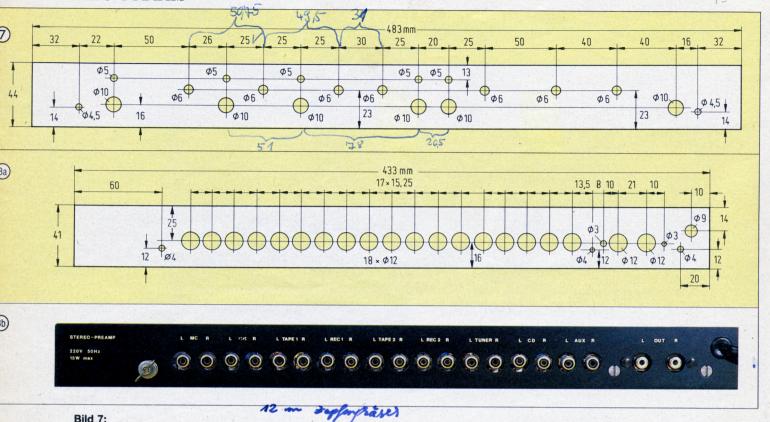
Beim Bearbeiten der Frontplatte sollten Sie diese zwischen Holz mit Zwingen festspannen.
